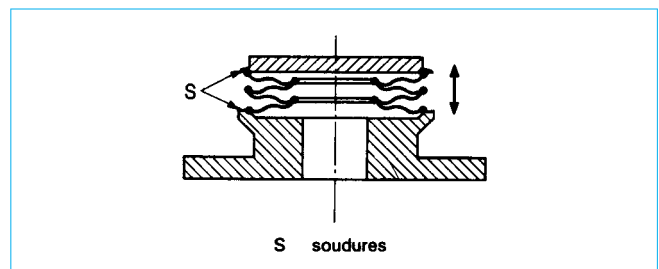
Étanchéité par soufflet à disques soudés
